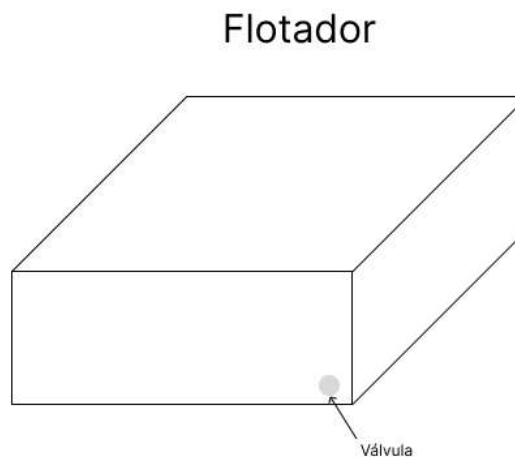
Posición de válvula en flotador Fuente: elaboración del autor
